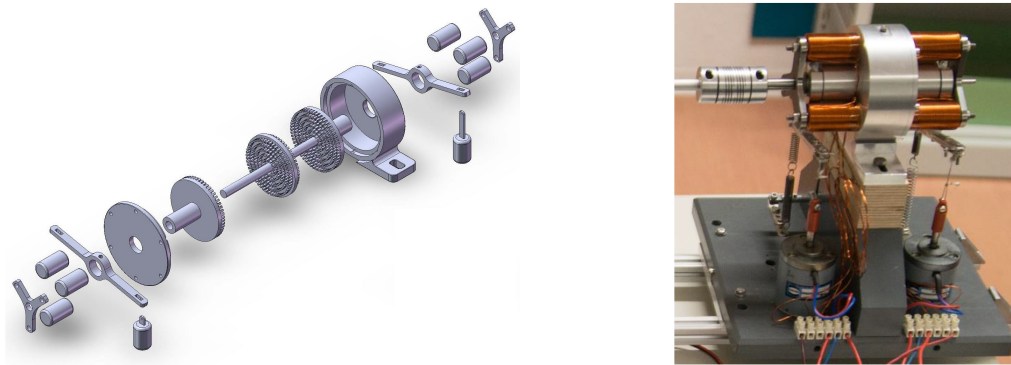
Explosionszeichnung des rotatorischen MRF-basierten Vibromotors (links) und Prototyp-Aufbau mit Wellrohrkupplung(rechts)
